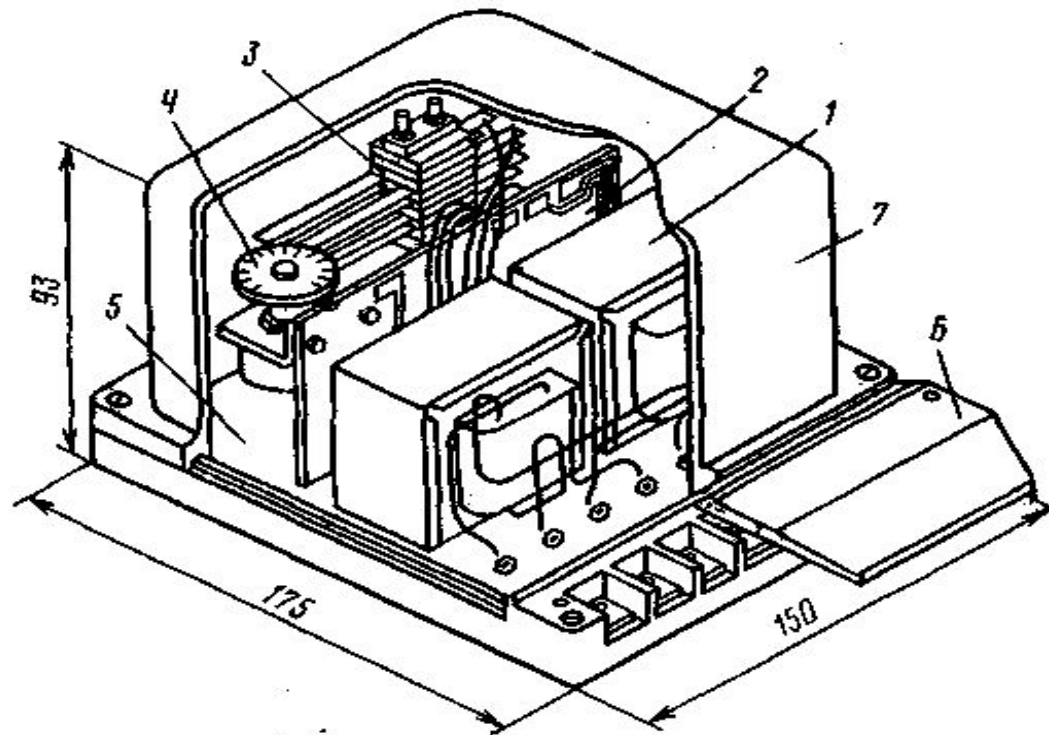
Модернизированное фазочувствительное устройство защиты ФУЗ-М: 1 — трансформатор тока; 2 — печатная плата; 3 - реле защиты; 4 — шкала потенциометра; 5 — изоляционное основание; 6 — крышка, закрывающая клеммную колодку; 7 — крышка
